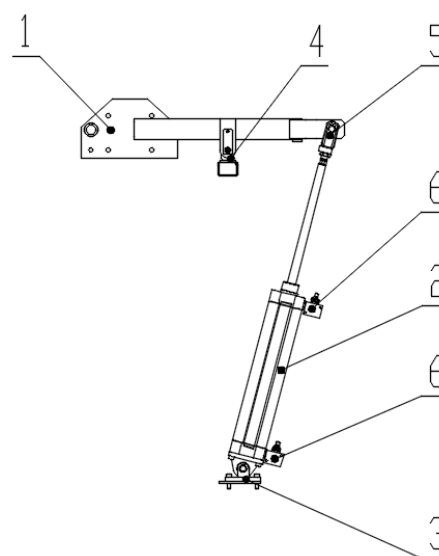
Устройство подъема погружного барабана: вид сбоку
